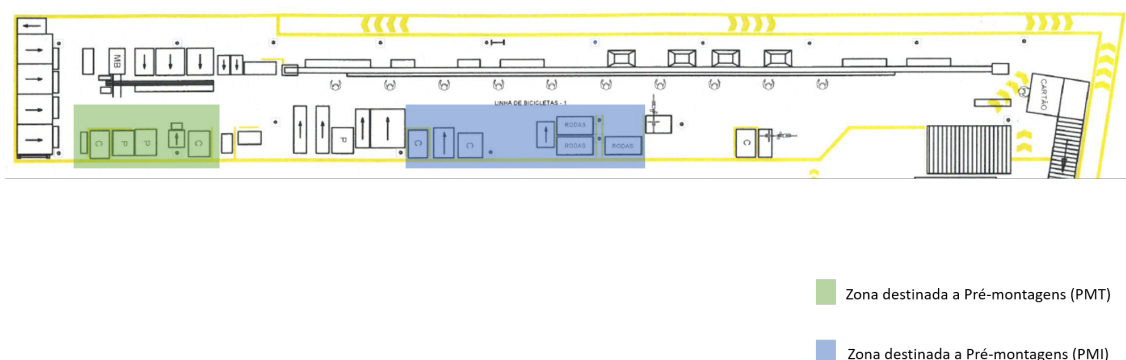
Planta da linha 1 com zonas destinadas a pré-montagens assinalada
